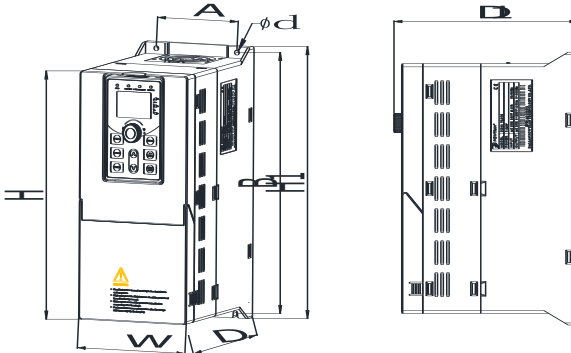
Dimensões de contorno 5.5~11kW G3 (Chassis No.: A3)
